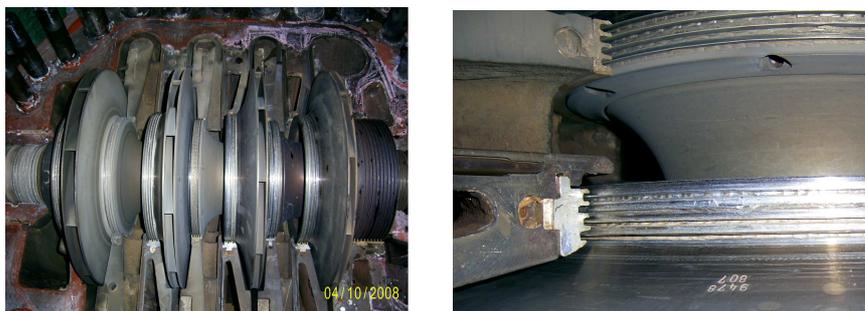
Лабиринтные уплотнения новой конструкции в корпусе сжатия
